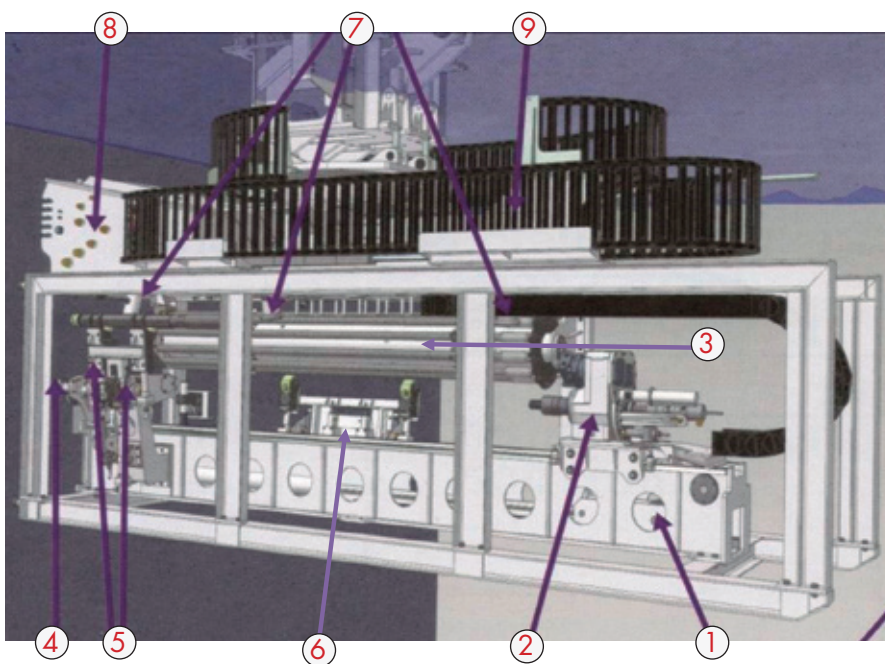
Detalhe esquemático da perfuratriz submersa.
